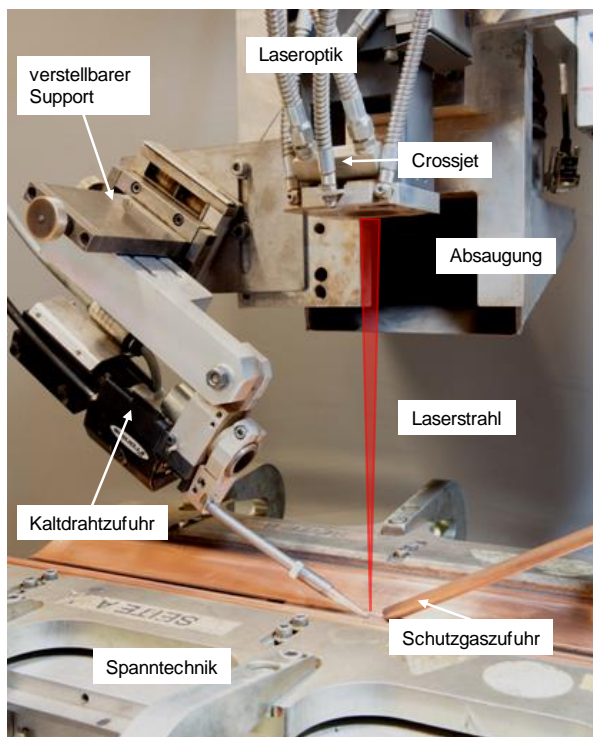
Versuchsaufbau der Schweißversuche mit Kaltdraht und Schutzgas
